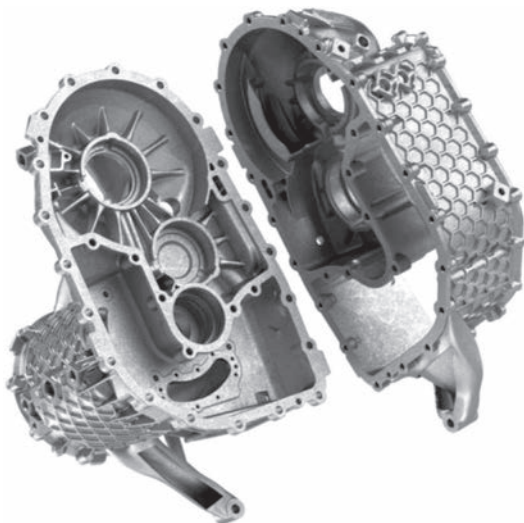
Корпус силового агрегату, створений способом SLM за допомогою установки NXG XII 600 [20]
